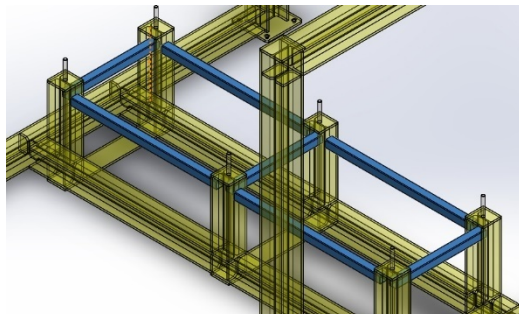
Detalle tubos cuadrados de refuerzo
